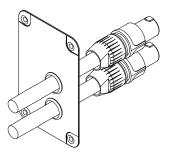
Connexion câble NL4 avec plaque de protection [1]
